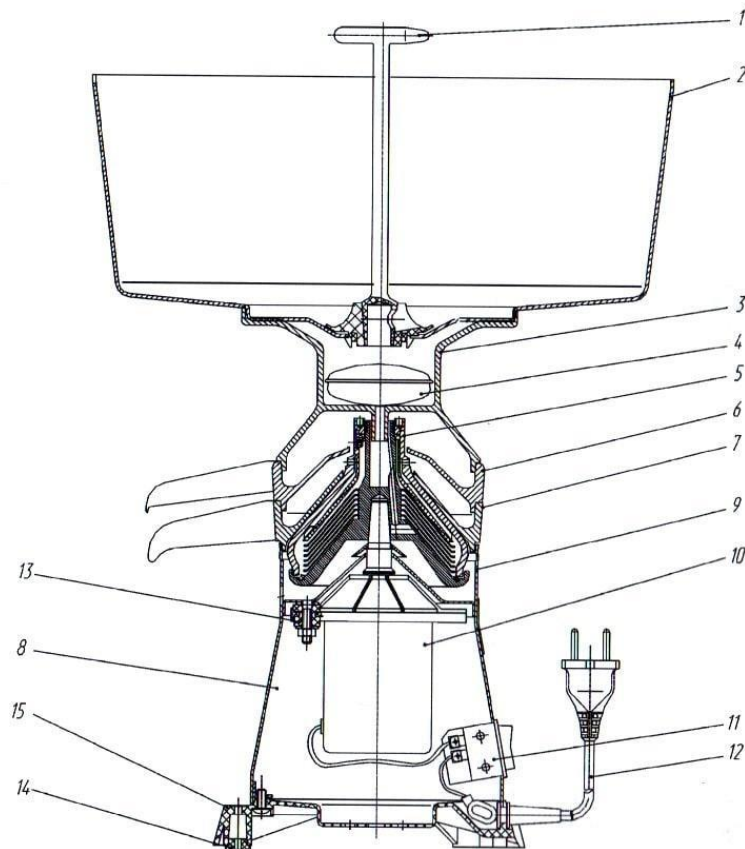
Схематичне зображення конструкції сепаратора
